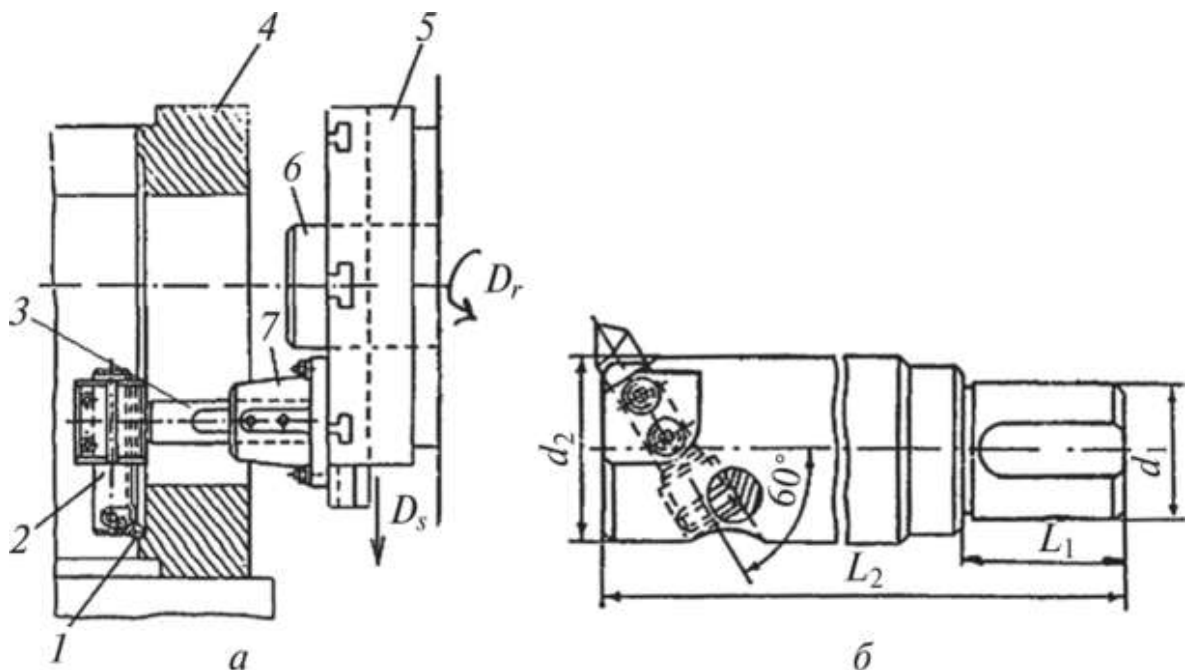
Схема підрізування торця консольною борштангою
